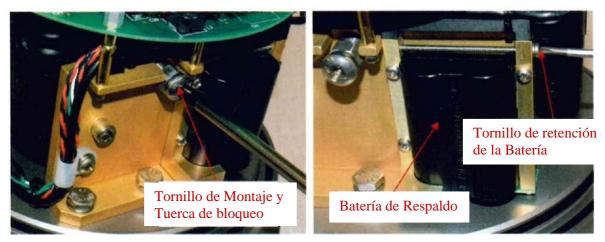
Cámara Instalada e Instalando la Batería de Respaldo
